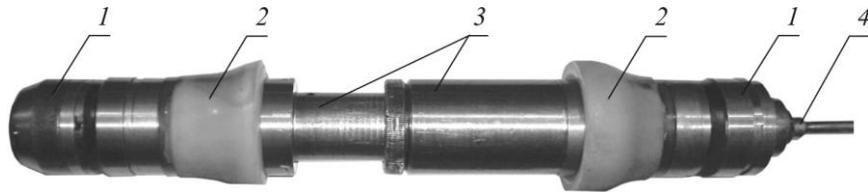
Общий вид пакера с гидравлическим механизмом сжатия: 1 — корпус; 2 — полиуретановая полуvtулка; 3 — гидравлический цилиндр; 4 — штуцер
